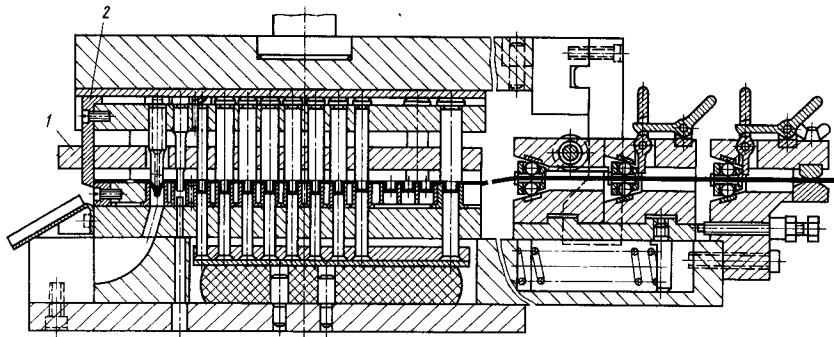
Штамп для последовательной вытяжки деталей типа пистона с автоматической роликоклиновой подачей
